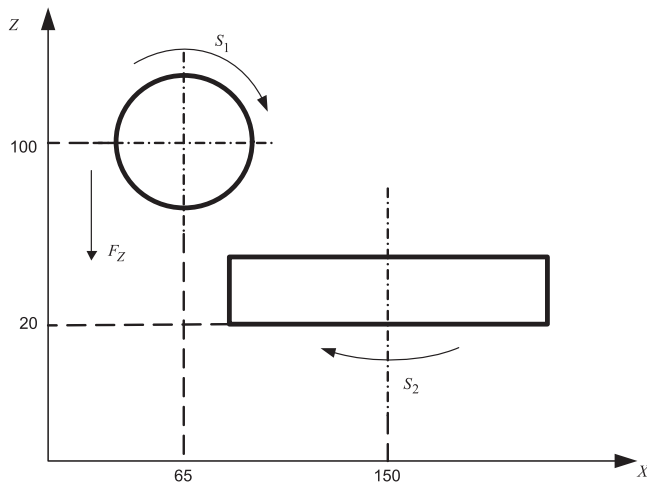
Схема обработки цилиндрического прямозубого колеса
